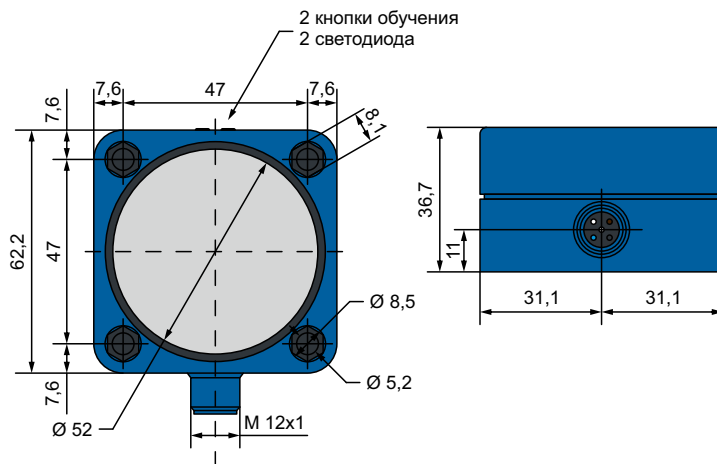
Габаритные размеры датчиков Ics+600/...
